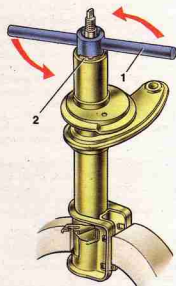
Отворачивание гайки корпуса стойки: 1 – ключ 67.7811.9510; 2 – гайка
